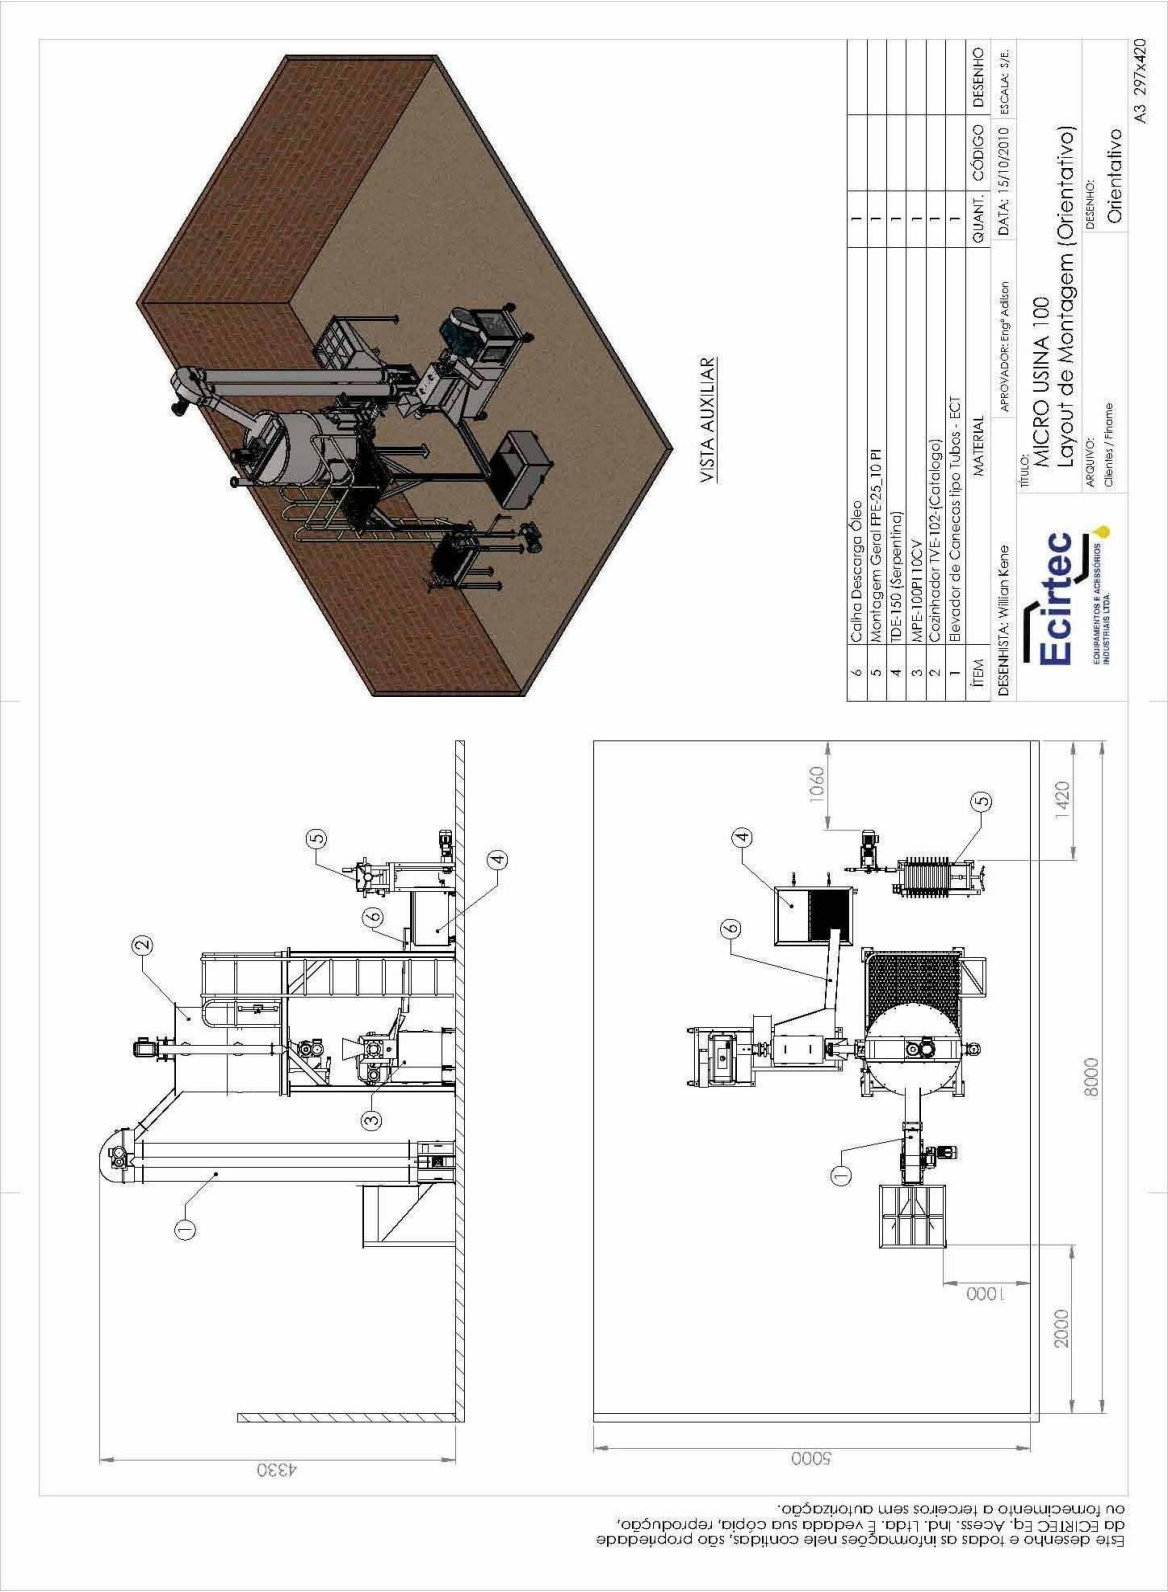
LAYOUT DE MONTAGEM DOS EQUIPAMENTOS
